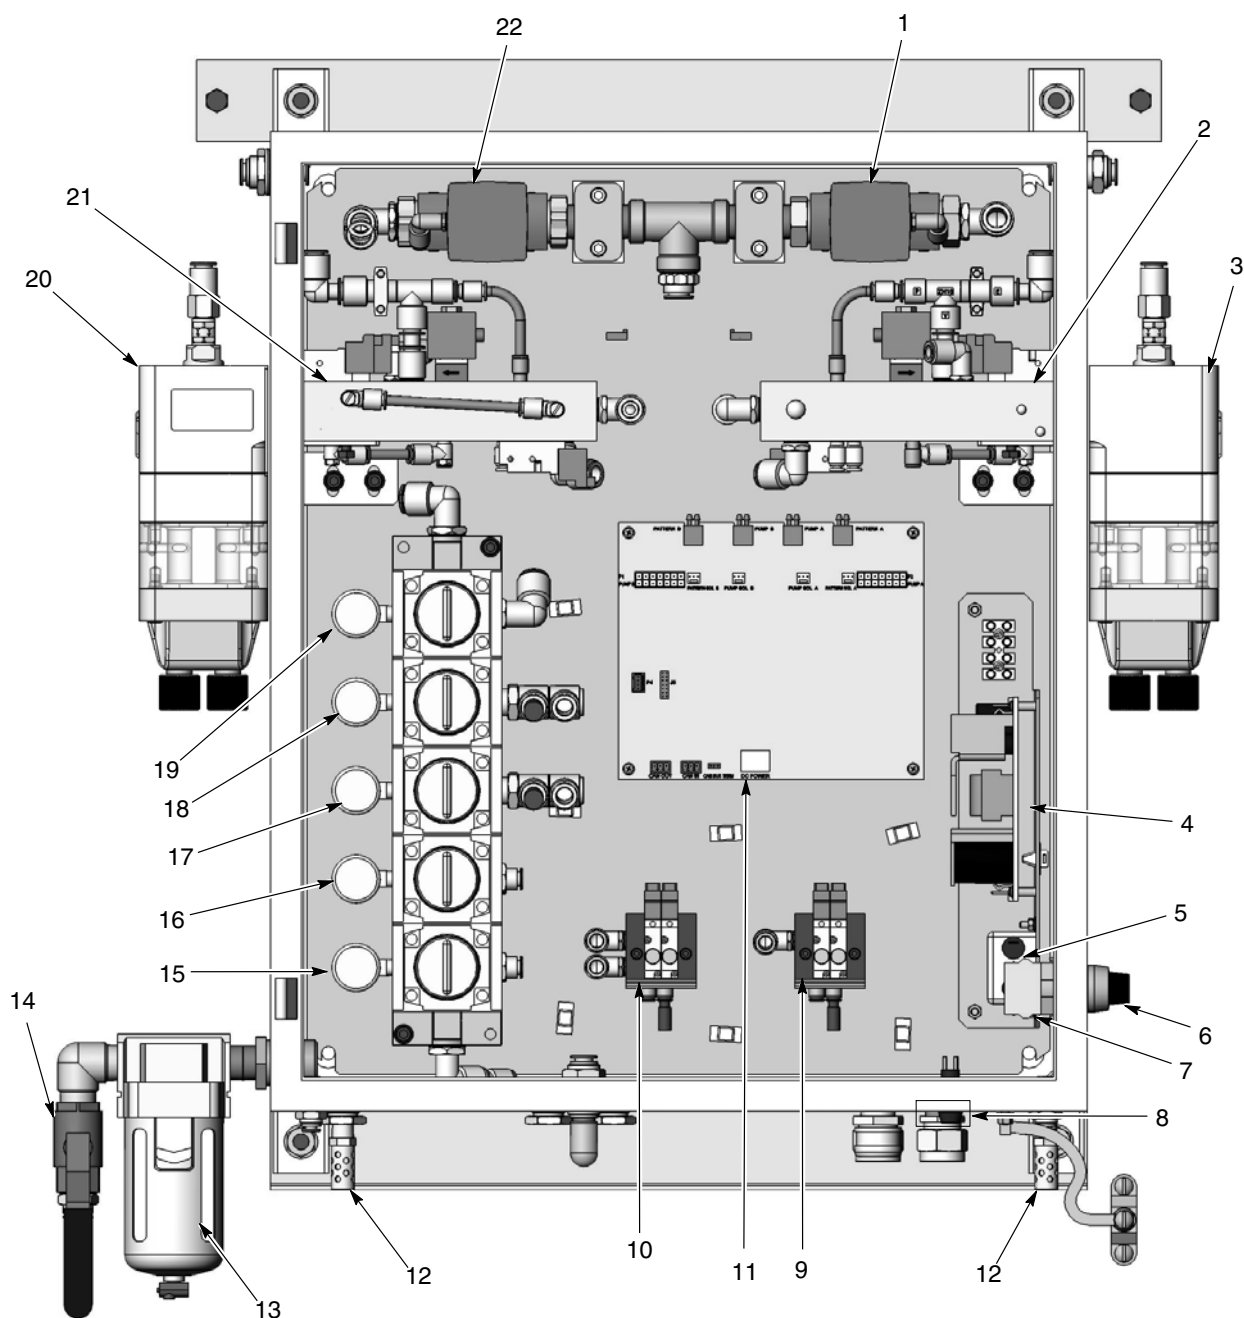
Pumppanelens komponenter (två-pistolers system visat)
